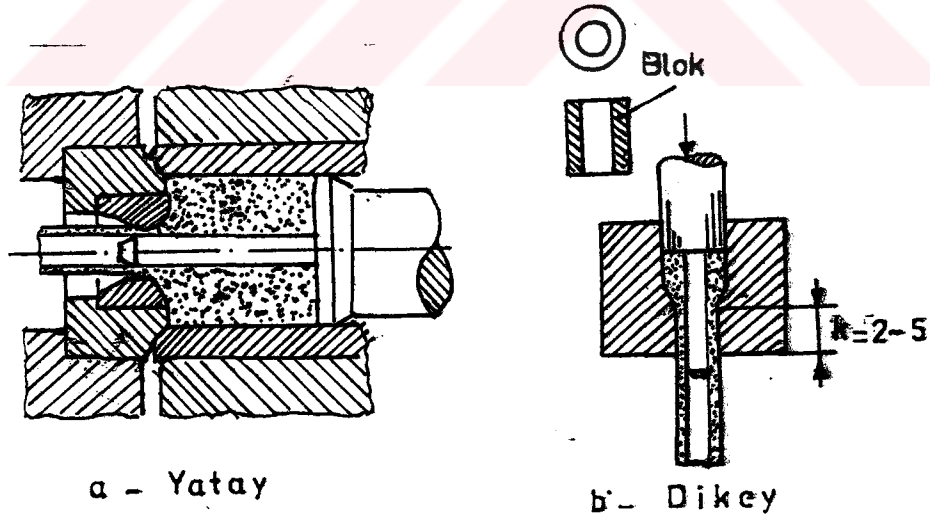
Ekstrüzyonda kullanılan bazı istanpalar.
